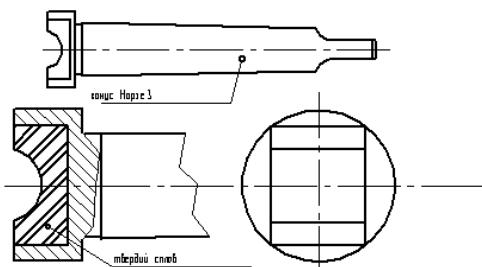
Інструмент для формування головки невипадаючої ручки приводу свердла електричного колонкового СЕК-1
